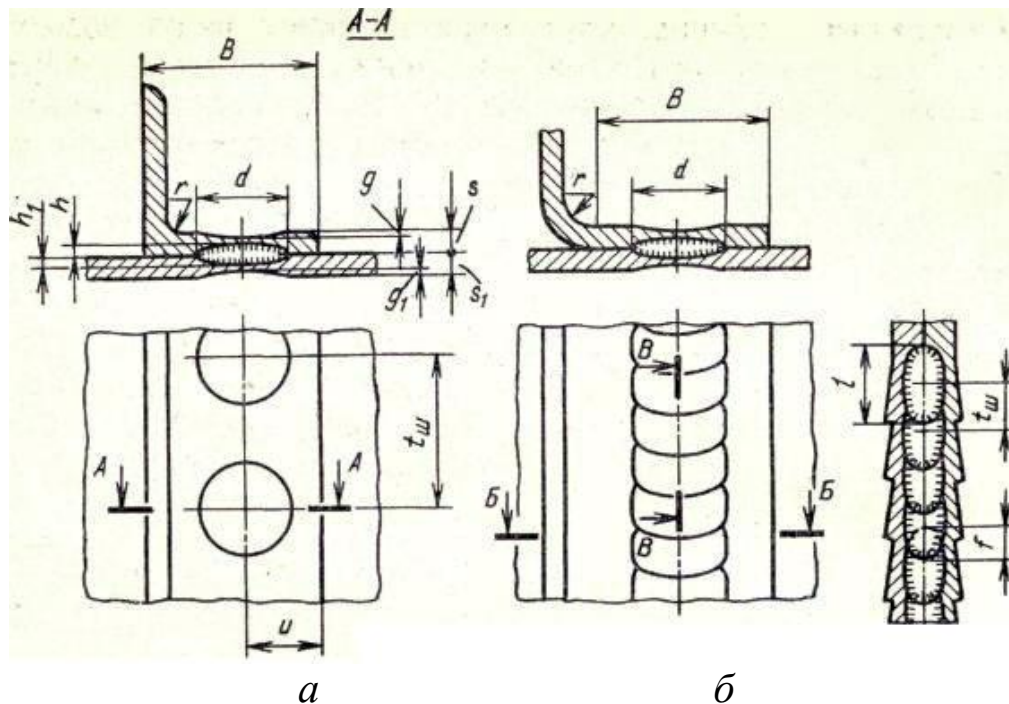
Конструктивные элементы соединений при сварке:
